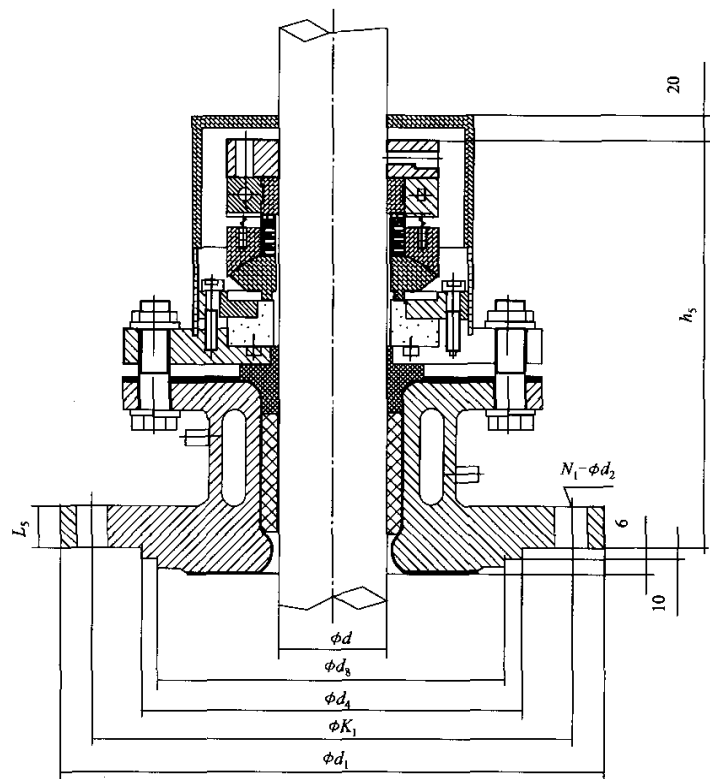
212 型机械密封结构尺寸图  $d \leq 95$  mm
